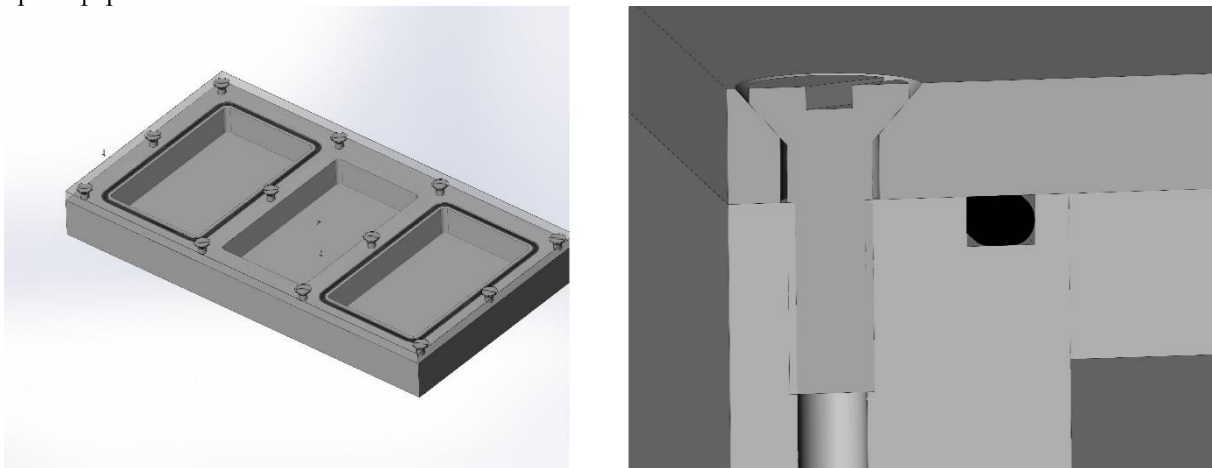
Установка крышки с прокладкой из проводящей резины.
